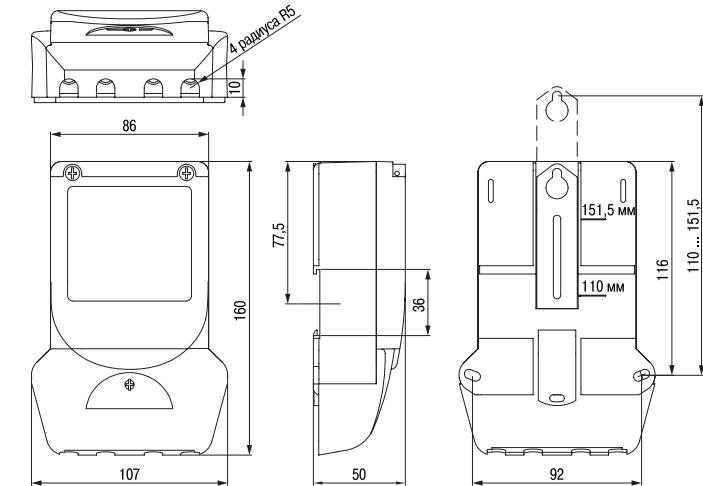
Габаритные и присоединительные размеры счётчиков габарита корпуса 4
